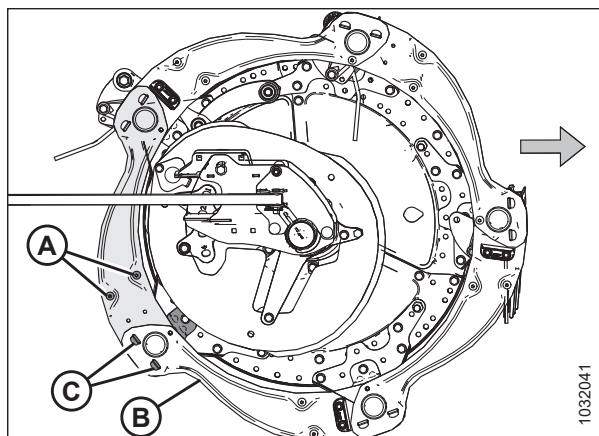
Бокові щитки мотовила — зовнішній кінець ексцентрика
